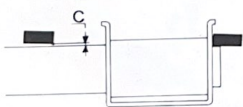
Posición de las patas de la horquilla, C: Lado interior, puede alcanzar un valor de 3 mm.
